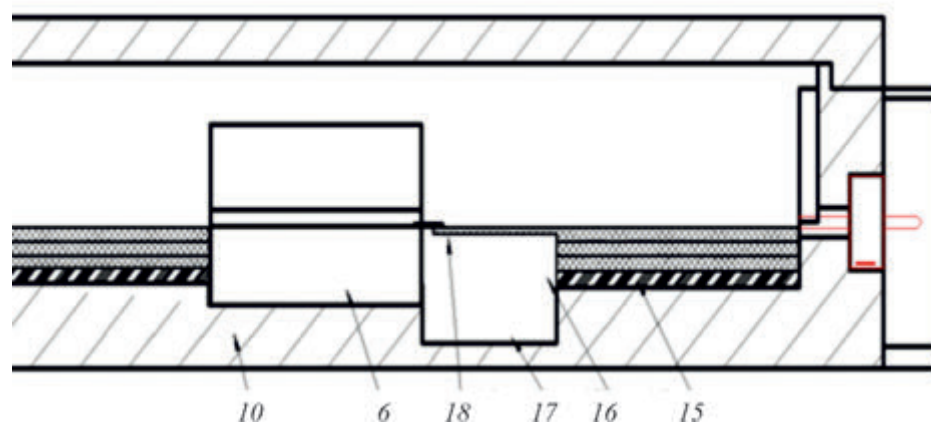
ГИС СВЧ-диапазона с 3D-компоновкой элементов и компонентов, а также с металлическим основанием и углублением в дне корпуса: 6 – КДР; 10 – корпус; 15 – металлическое основание; 16 – края отверстия металлического основания; 17 – углубление в дне корпуса; 18 – углубление на обратной стороне верхнего диэлектрического слоя МПП
